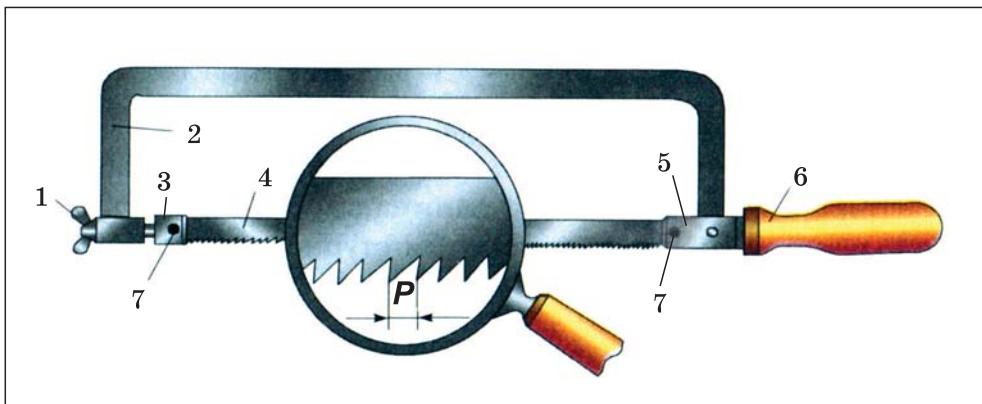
Ручная слесарная ножовка: 1 – натяжная гайка; 2 – рамка; 3 – подвижная головка; 4 – ножевочное полотно; 5 – неподвижная головка; 6 – ручка; 7 – штифты
